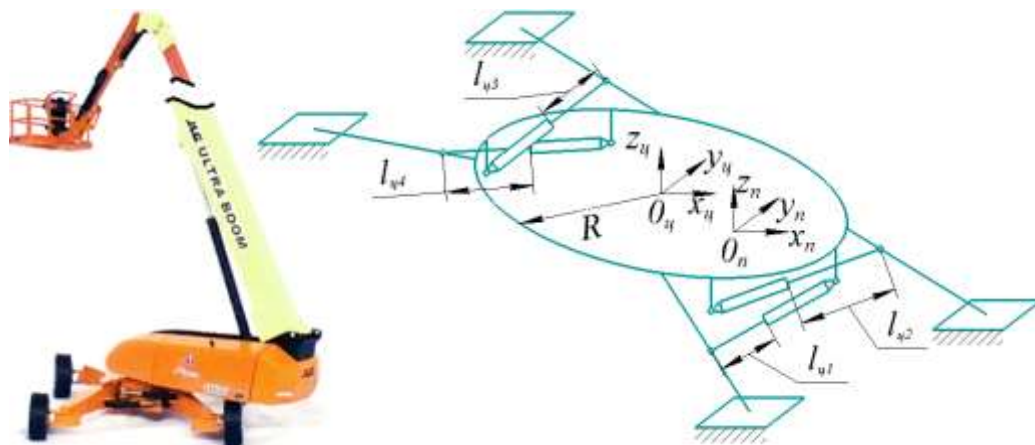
Опорний пристрій МПРП з механізмом регулювання бази машини
